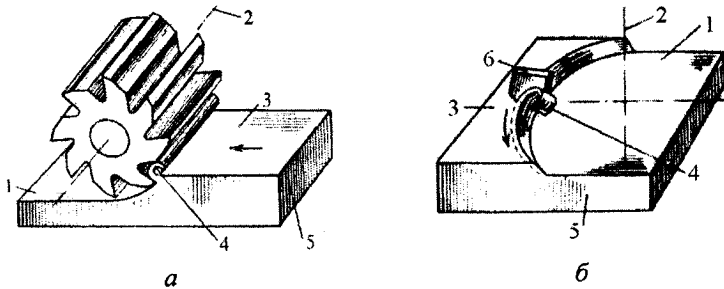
Схеми фрезерування: а – циліндричного; б – торцевого; 1 – оброблена поверхня; 2 – вісь обертання фрези; 3 – подача; 4 – стружка; 5 – деталь; б – ніж фрези
